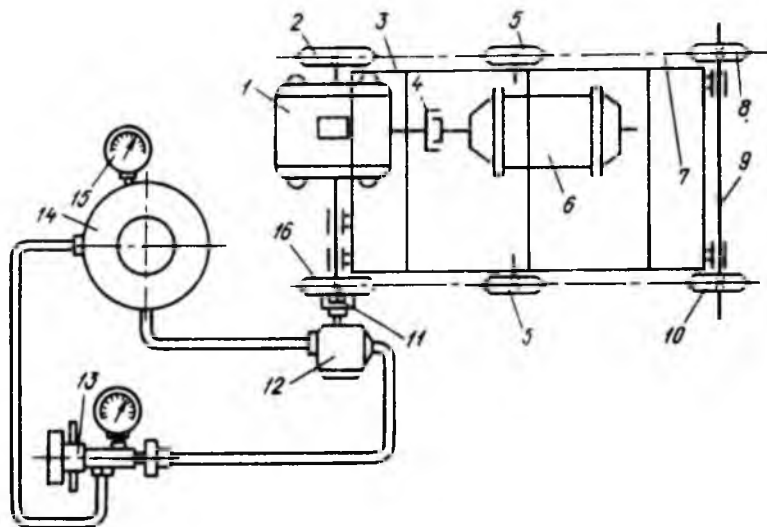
Стенд для обкатки цепных передач (Целинный филиал ГосНИТИ):
